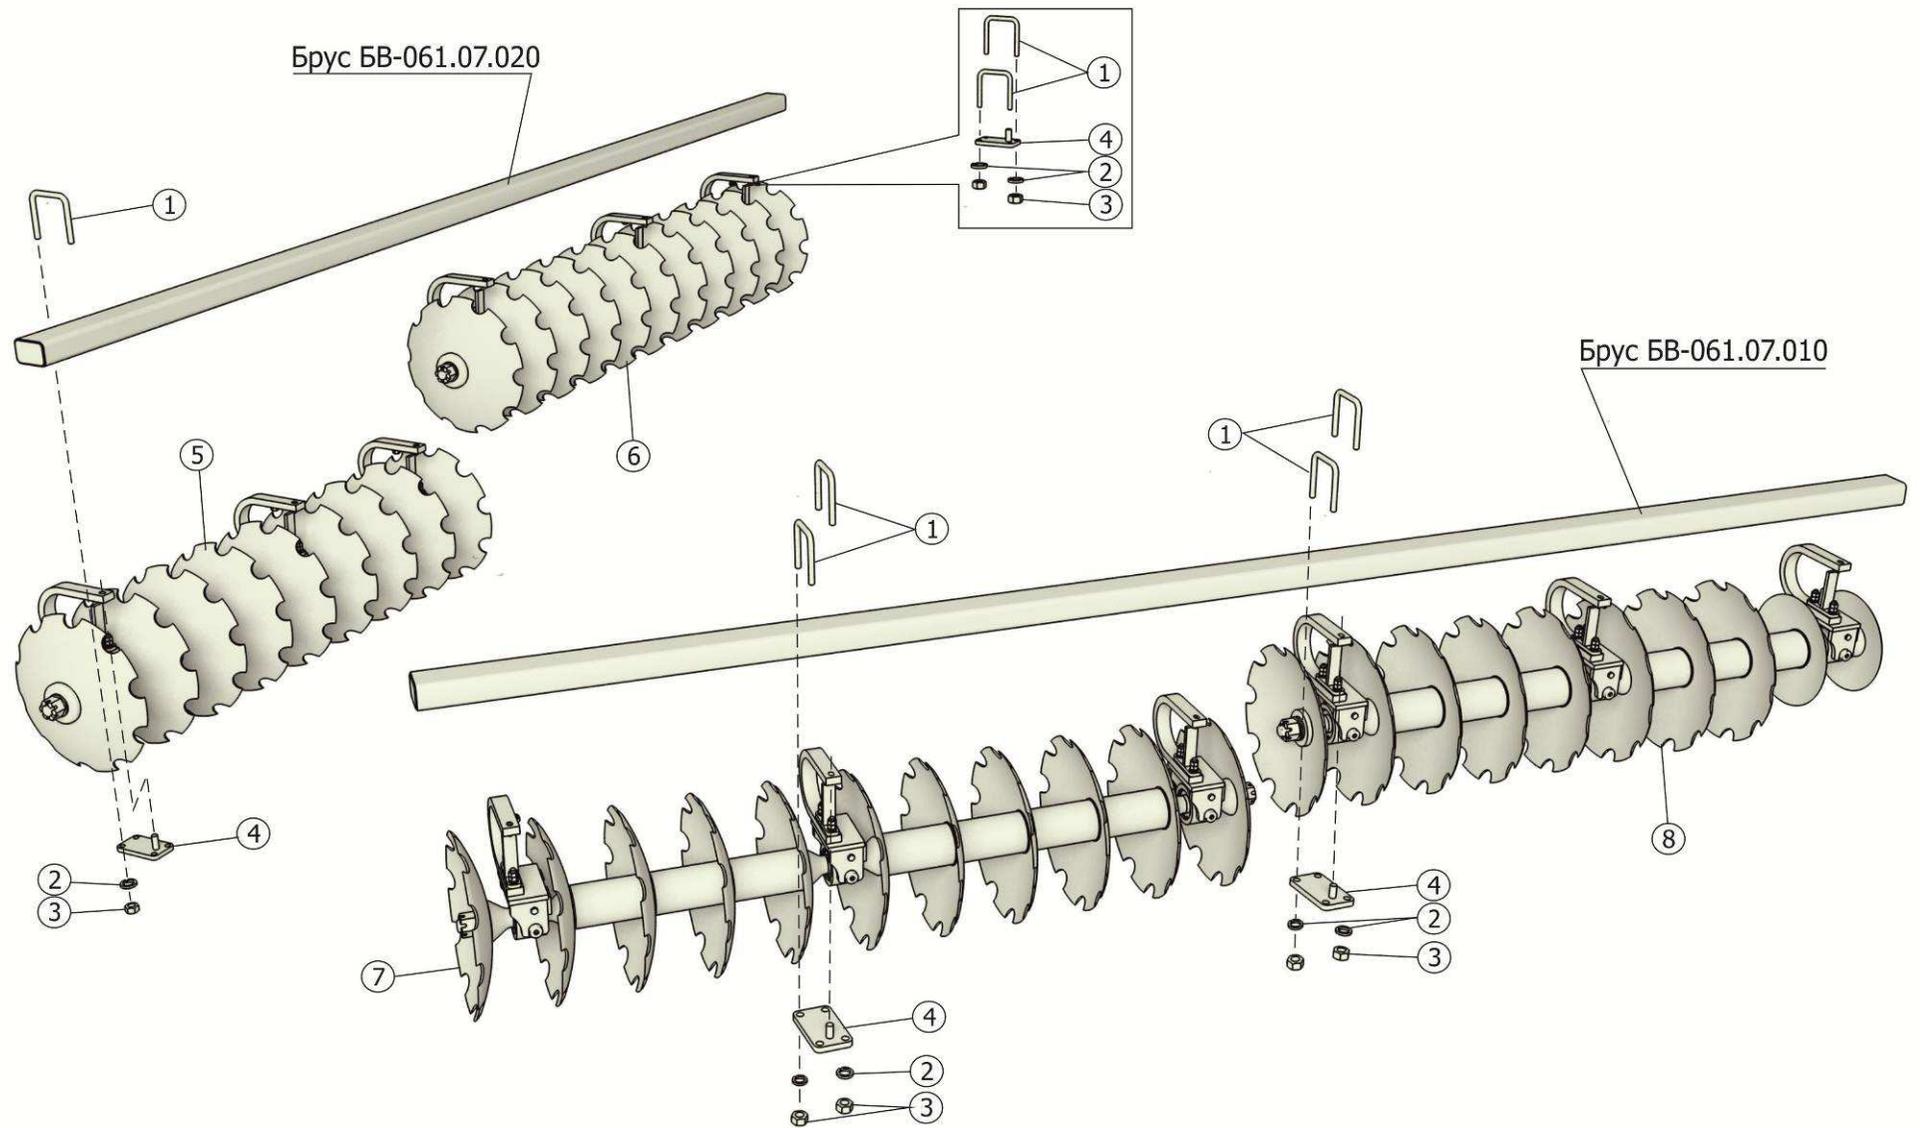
Установка дисковых батарей БВ-061.03.000А
